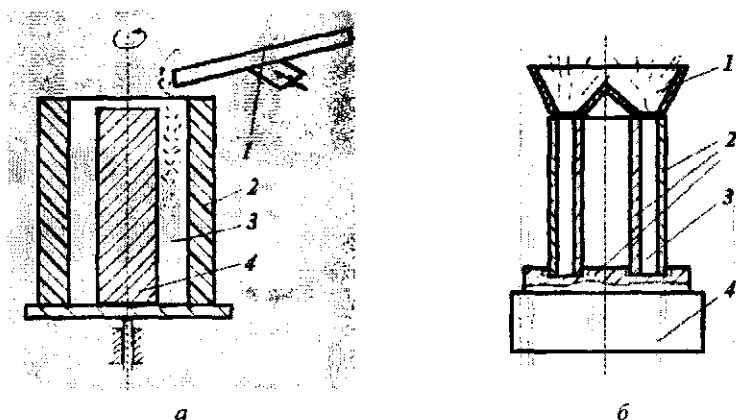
Схемы процессов воздушного войлокования для получения трубчатых волоконных материалов: а – методом изостатического прессования (1 – вибрирующий дозатор; 2 – эластичная оболочка; 3 – кольцевой зазор; 4 – металлический формообразующий стержень); б – спеканием со свободной засыпкой (1 – загрузочная воронка; 2 – форма для спекания; 3 – кольцевой зазор; 4 – вибрирующее устройство)
